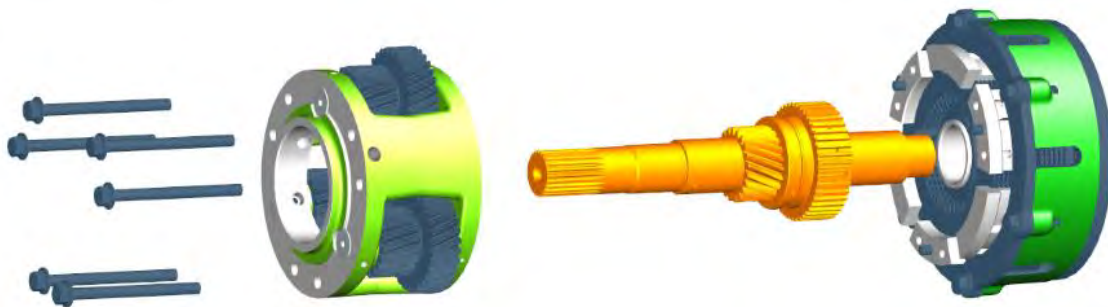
"Explosionado del montaje del portasatélites del eje de entrada"
